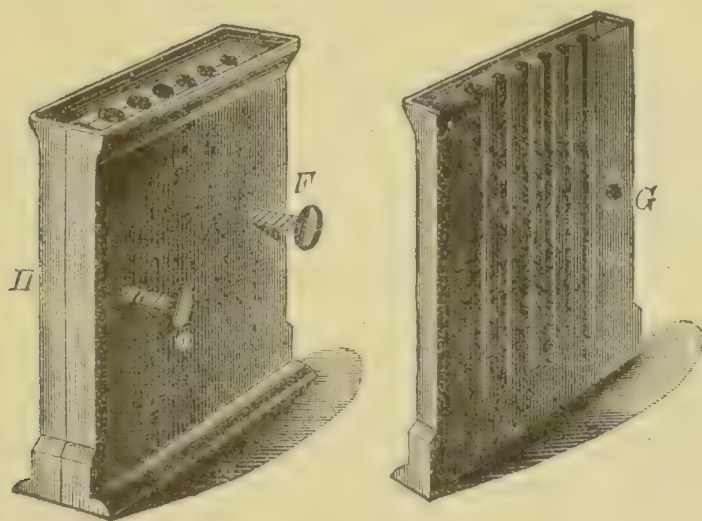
Lapisform oder Gussform zu Lapis causticus. H ganze Form; G eine Hälfte derselben.
